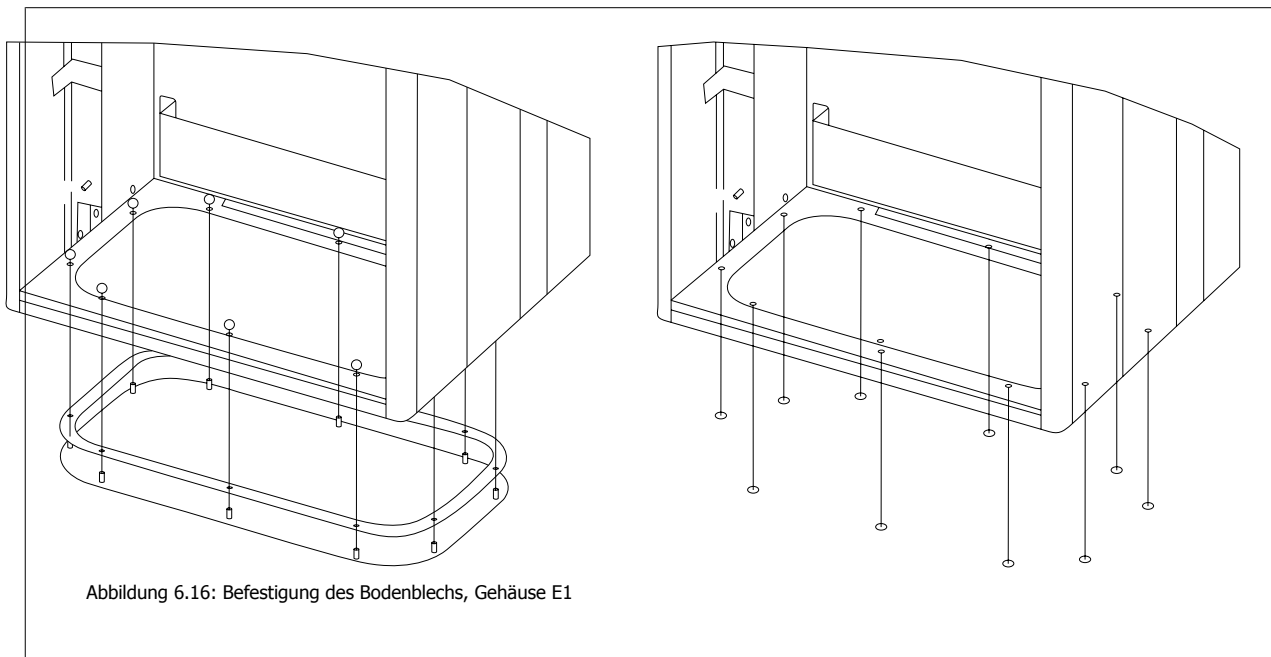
Befestigung des Bodenblechs, Gehäuse E1
